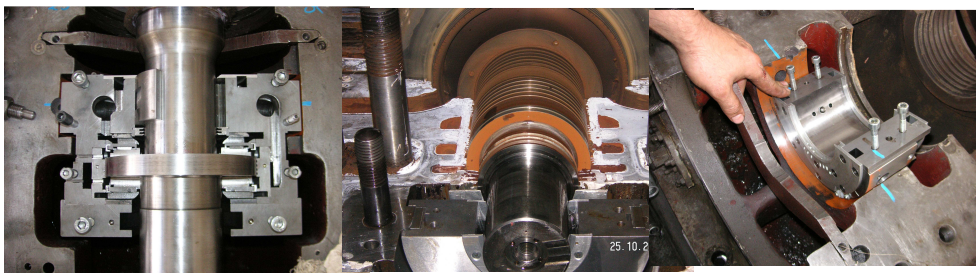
Демпферные подшипники для корпусов сжатия
